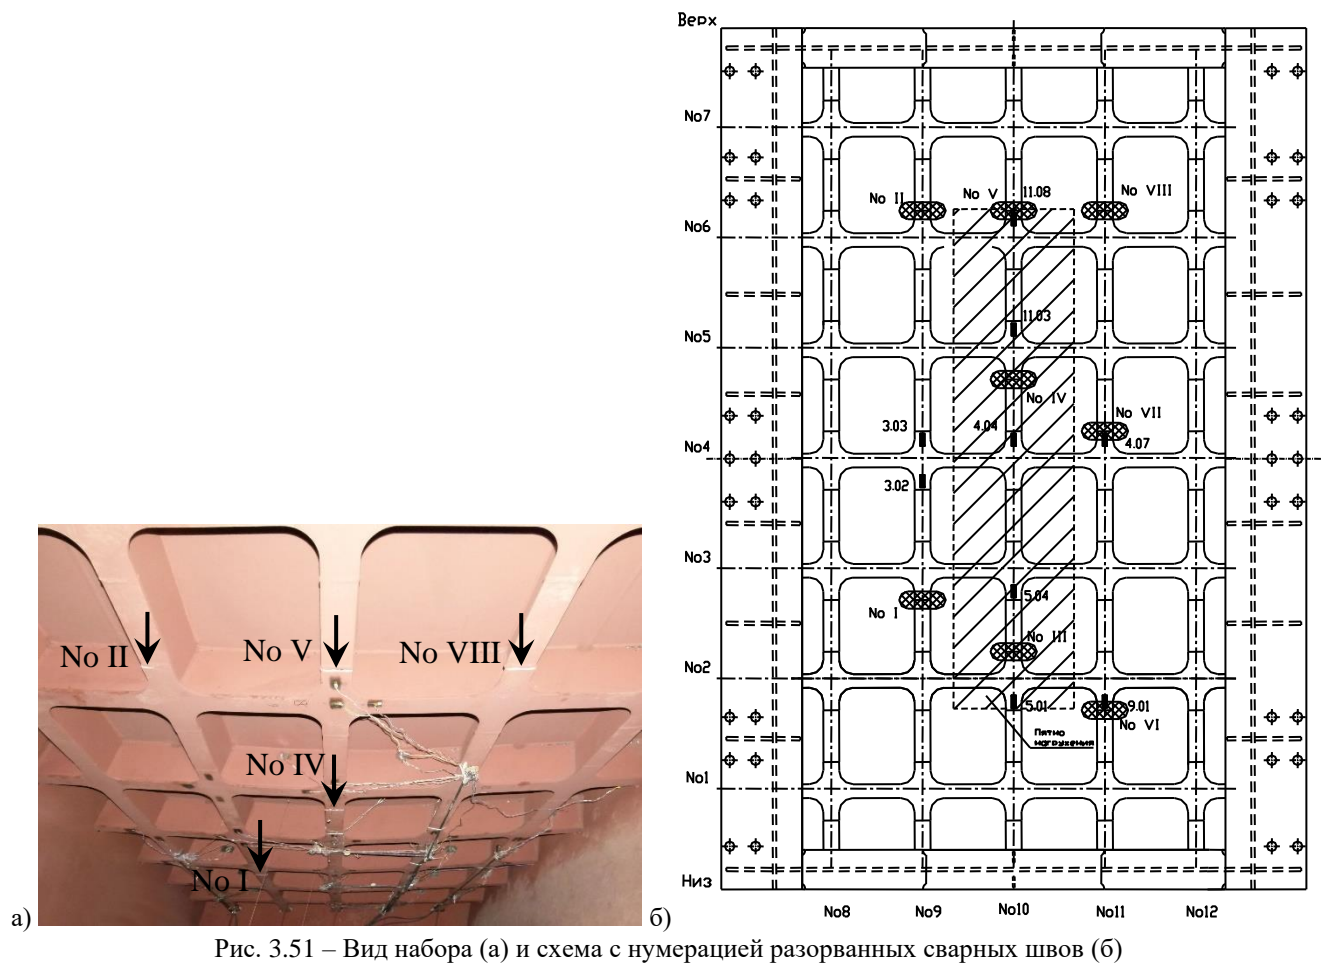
Вид набора (а) и схема с нумерацией разорванных сварных швов (б)
